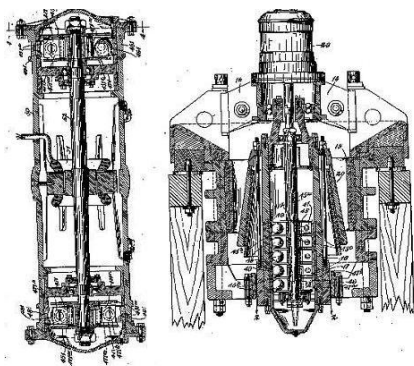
Рабочее колесо для вибраторов и дробилок.
